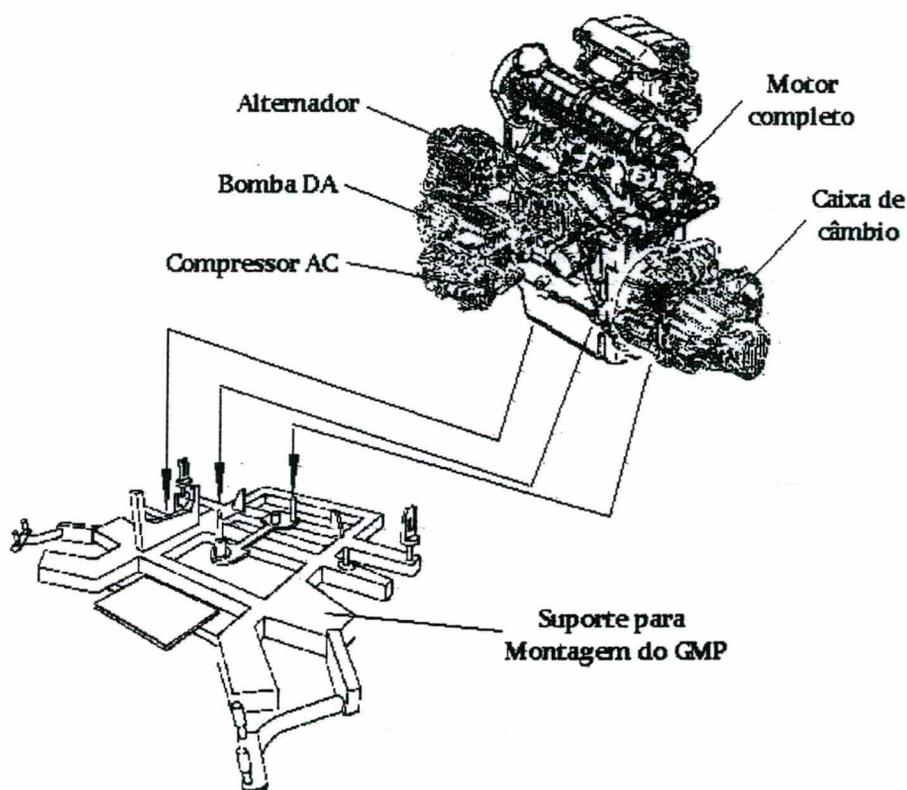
Desenho esquemático do conjunto motor, destacando suas principais peças e o suporte de montagem do GMP.
